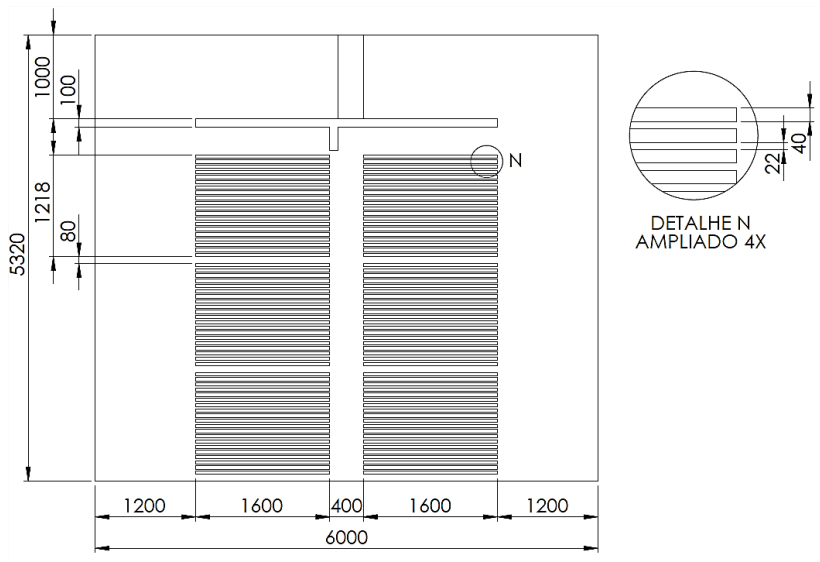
Detalhes e dimensões internas do modelo 1 – Vista em corte paralelo às laterais (Dimensões em mm).
